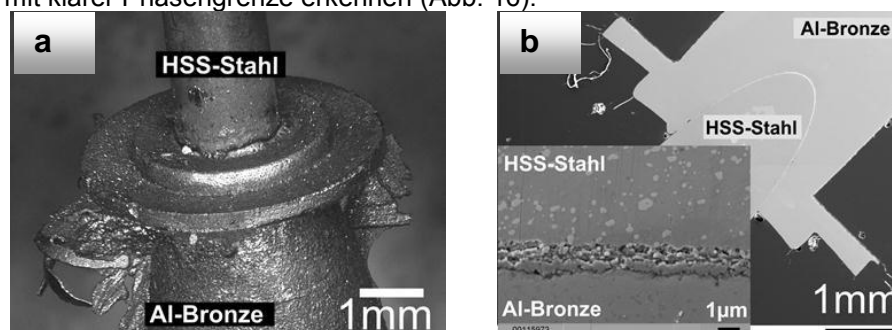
a) Verbundguss Werkzeugstahl-HSS mit Al-Bronze umgossen; b) REM Aufnahmen der Kontaktfläche
